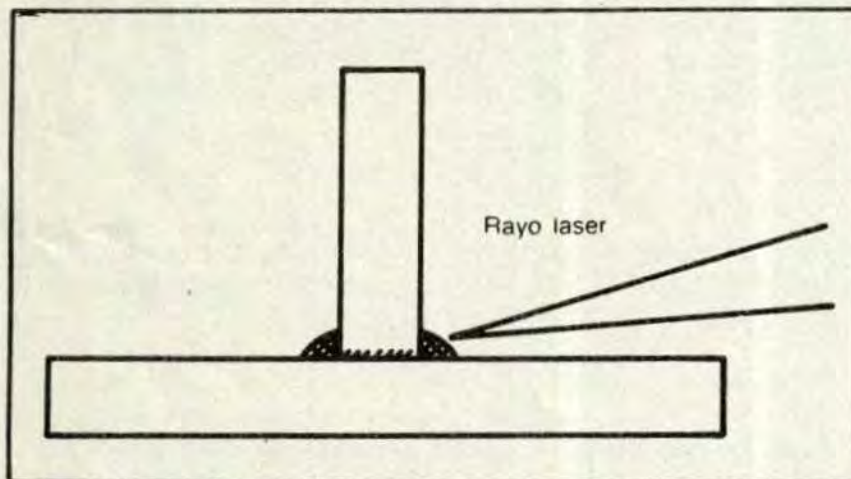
Soldadura de cordón discontinuo por láser de una junta en T.
